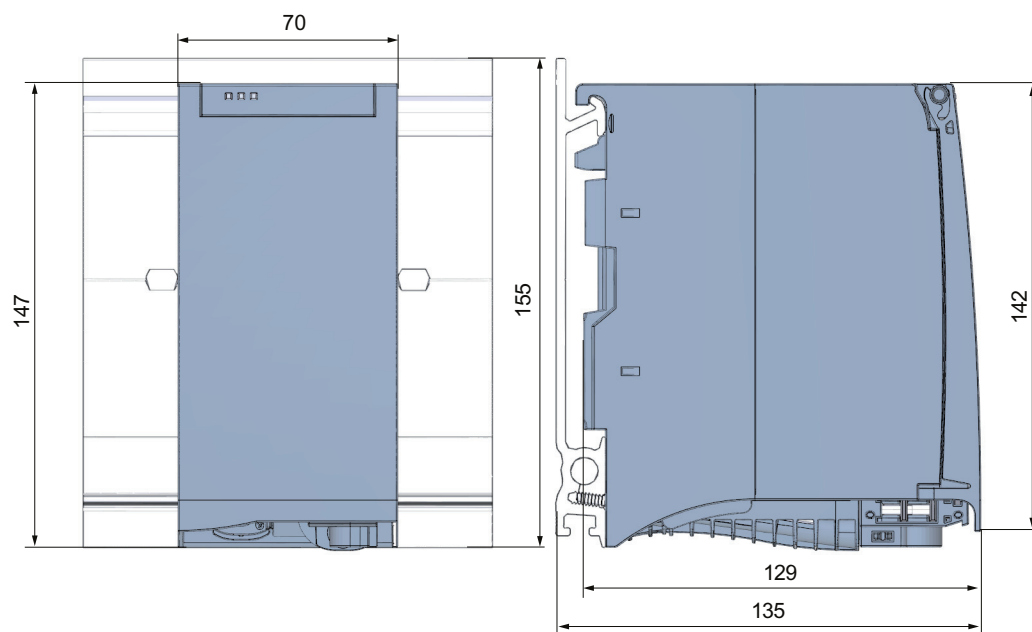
Габаритный чертеж блока питания PS 60W 120/230V AC/DC
